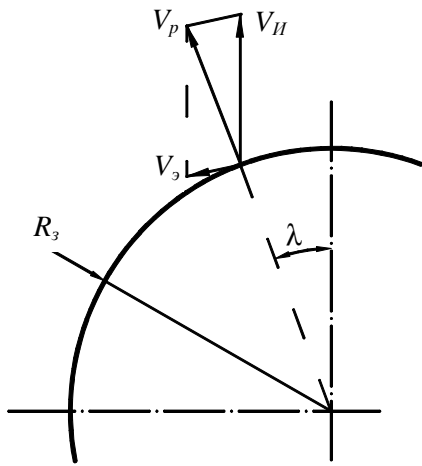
Схема направления скоростей при обработке торцового зубчатого контура
